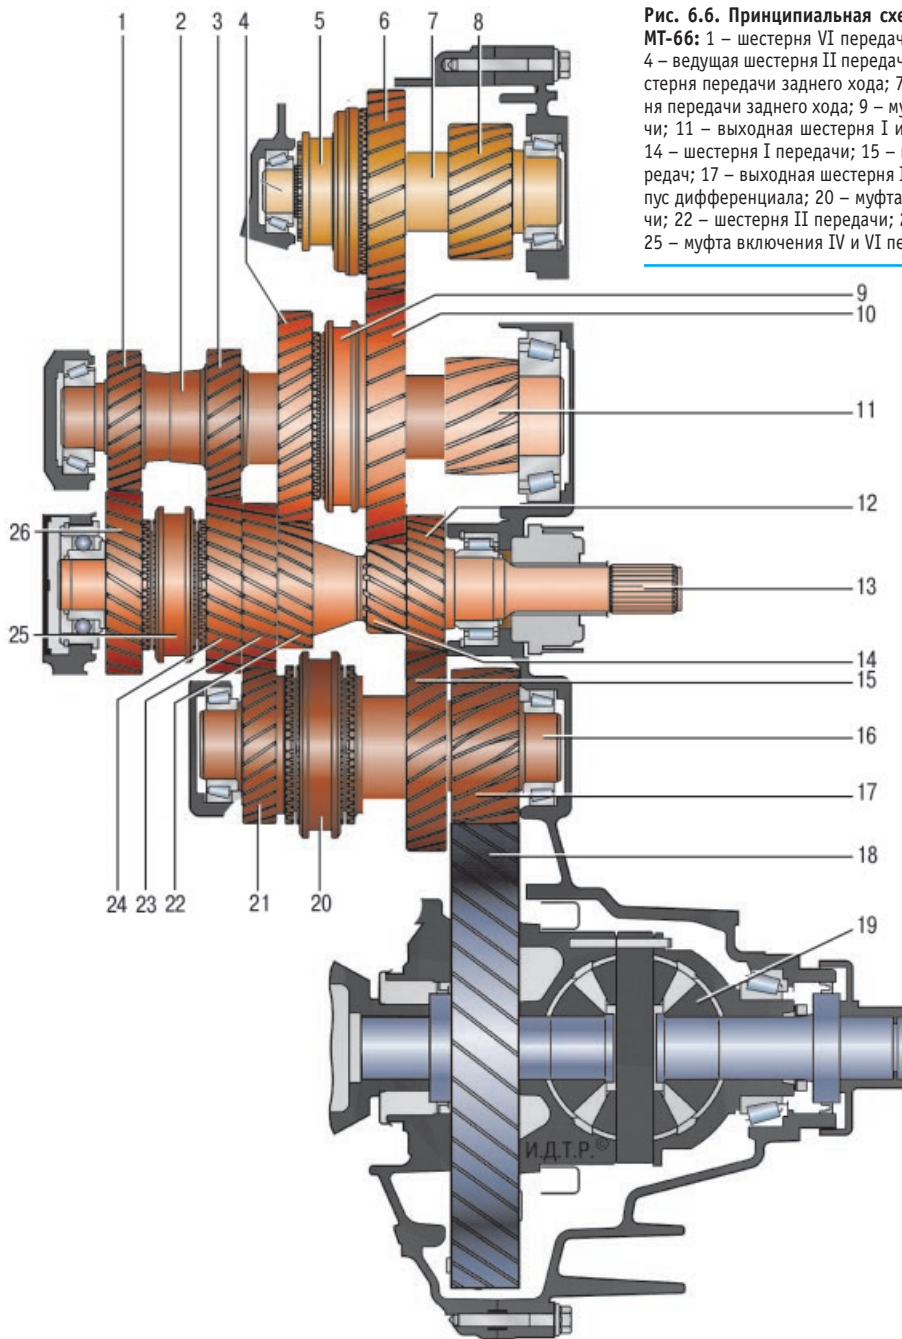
Принципиальная схема шестиступенчатой механической коробки передач мод. МТ-66: 1 – шестерня VI передачи; 2 – вторичный вал I и II передач; 3 – шестерня V передачи; 4 – ведущая шестерня II передачи; 5 – муфта включения передачи заднего хода; 6 – ведущая шестерня передачи заднего хода; 7 – вторичный вал передачи заднего хода; 8 – выходная шестерня передачи заднего хода; 9 – муфта включения I и II передач; 10 – ведущая шестерня I передачи; 11 – выходная шестерня I и II передач; 12 – шестерня III передачи; 13 – первичный вал; 14 – шестерня I передачи; 15 – ведущая шестерня III передачи; 16 – вторичный вал III и IV передач; 17 – выходная шестерня III и IV передач; 18 – ведомая шестерня главной пары; 19 – корпус дифференциала; 20 – муфта включения III и IV передач; 21 – ведущая шестерня IV передачи; 22 – шестерня II передачи; 23 – шестерня IV передачи; 24 – ведущая шестерня V передачи; 25 – муфта включения IV и VI передач; 26 – ведущая шестерня VI передачи
